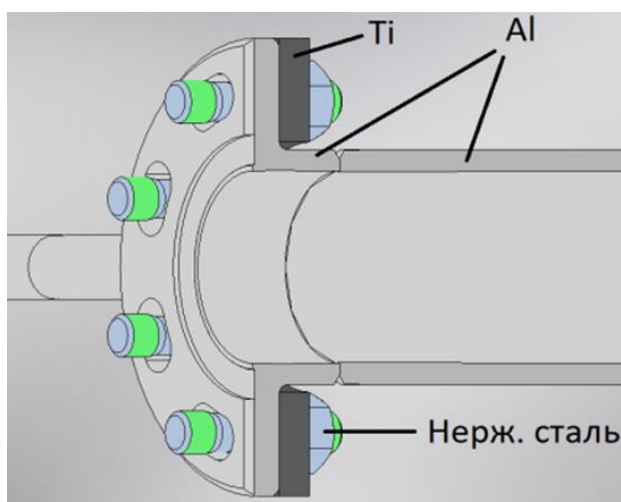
Схема поперечного сечения вакуумной камеры внутри патрубка откачного порта
